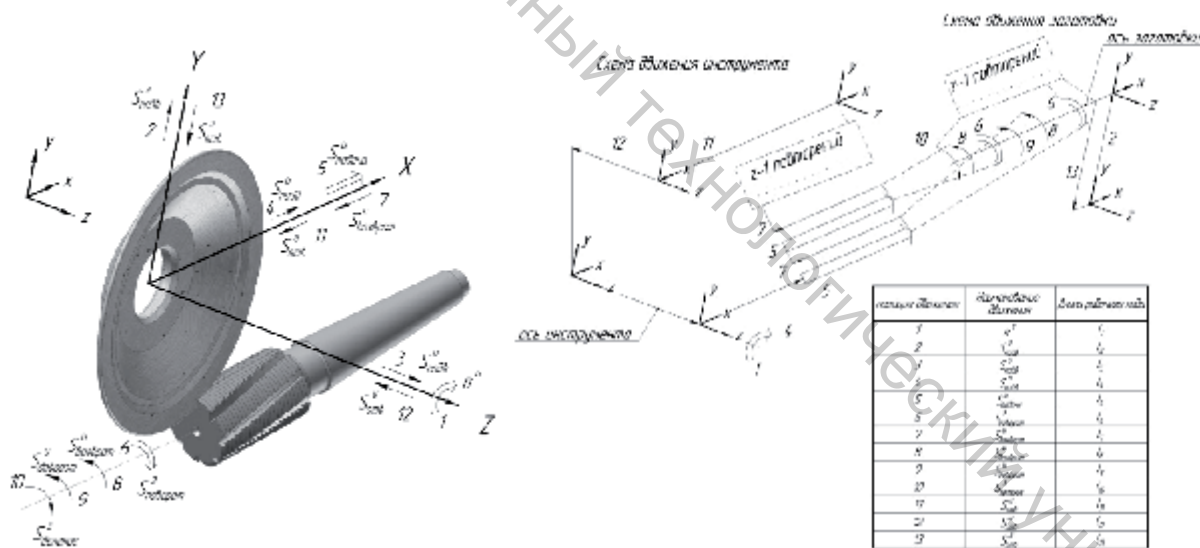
Пример схемы обработки и реализация движений по циклу заточки фрезы по передней поверхности
